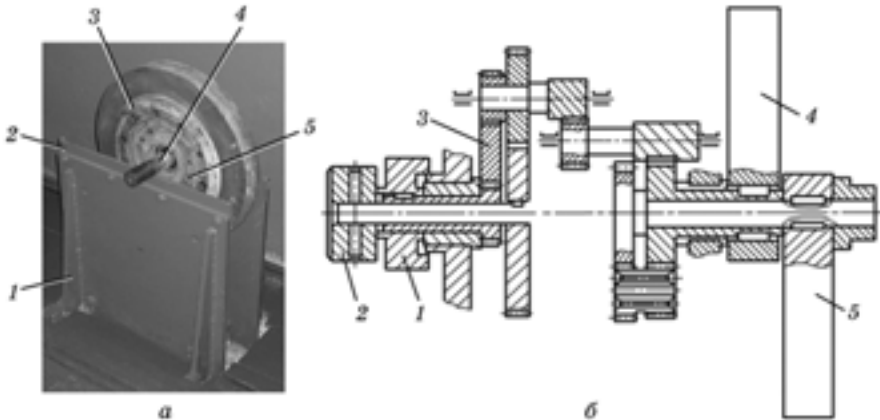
Зовнішній вигляд пристрою для статичного балансування (а) і схема пристрою для автоматичного балансування шліфувального круга на верстаті (б)
